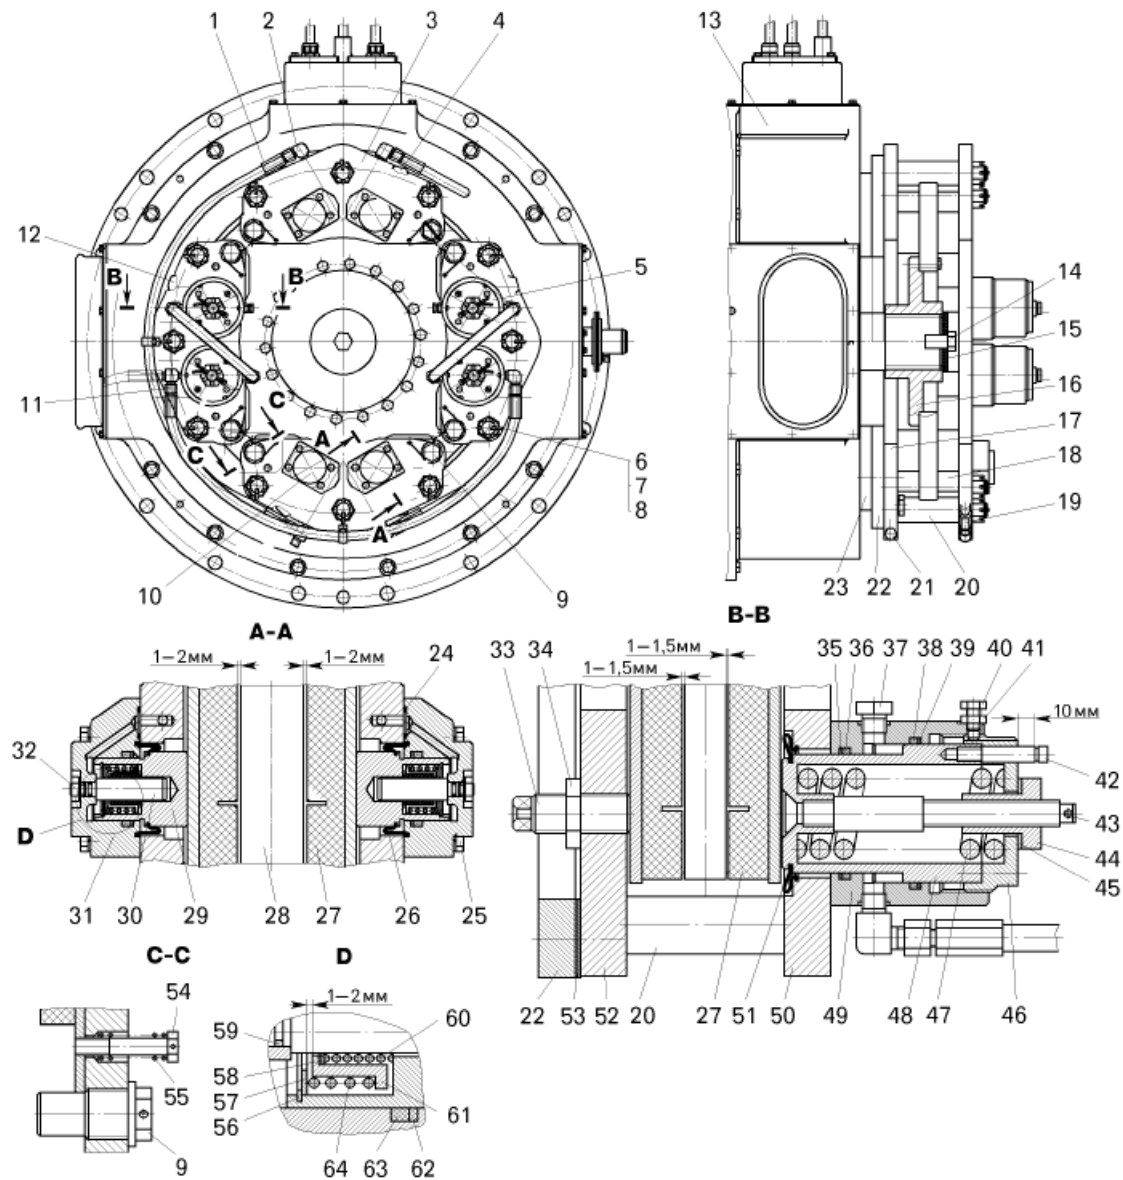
Тормозные механизмы задних колес и стояночного тормоза БелАЗ-7530 и 7531
